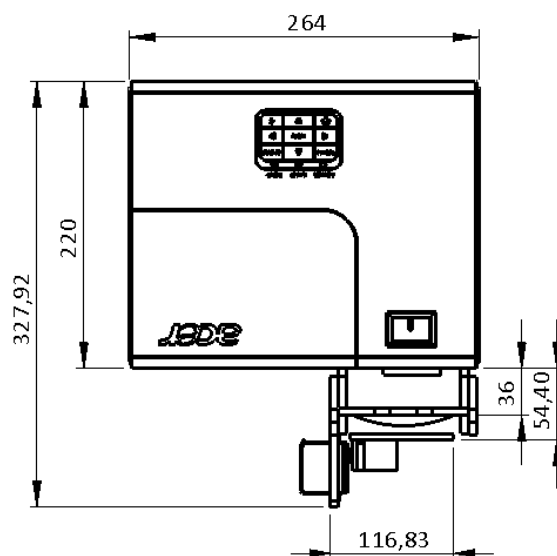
Esquema frontal dimensional del sistema óptico de la impresora.
